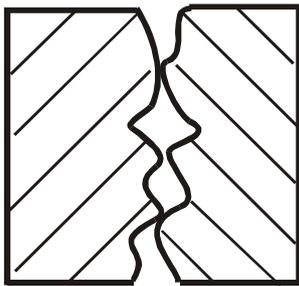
Фізичний контакт зварювальних поверхонь
